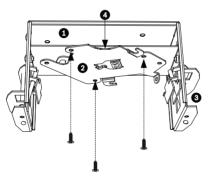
Fixar a placa de montagem ao suporte de montagem
